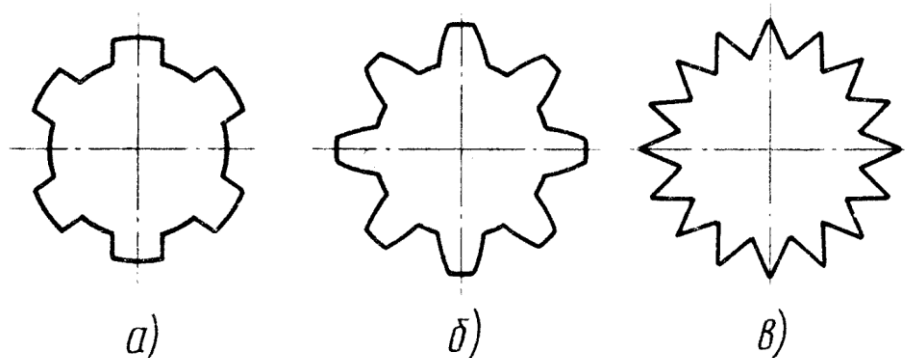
Профили зубьев шлицевых соединений: а – прямобочные, б – эвольвентные, в – треугольные.
